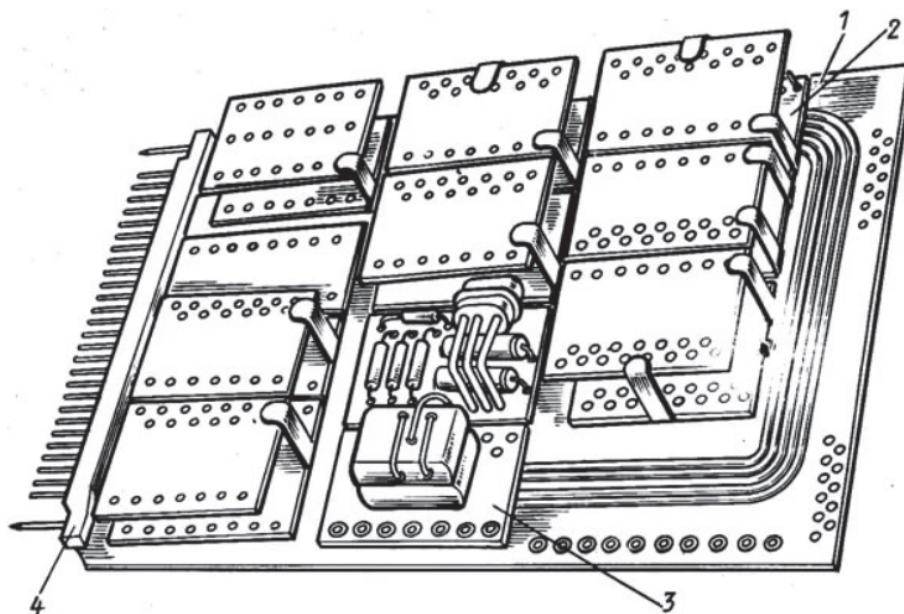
Компоновка ячейки ЭВМ второго поколения с использованием модулей на печатных платах: *1* – двусторонняя печатная плата; *2* – двухплатный модуль; *3* – одноплатный модуль; *4* – соединитель
